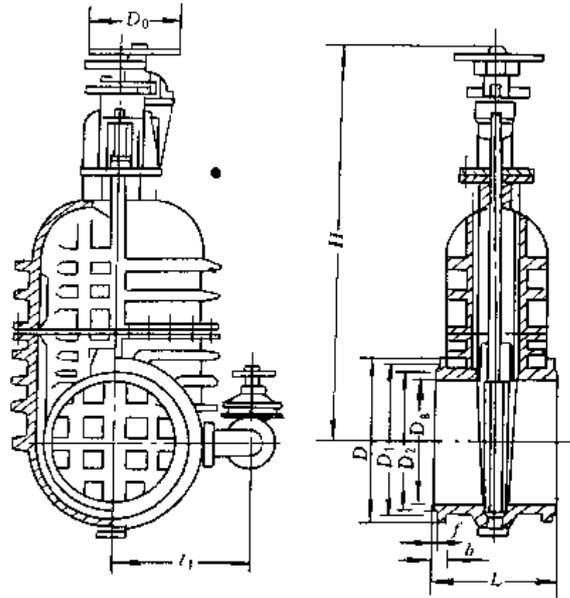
Z445T 型正齿轮传动暗杆楔式
